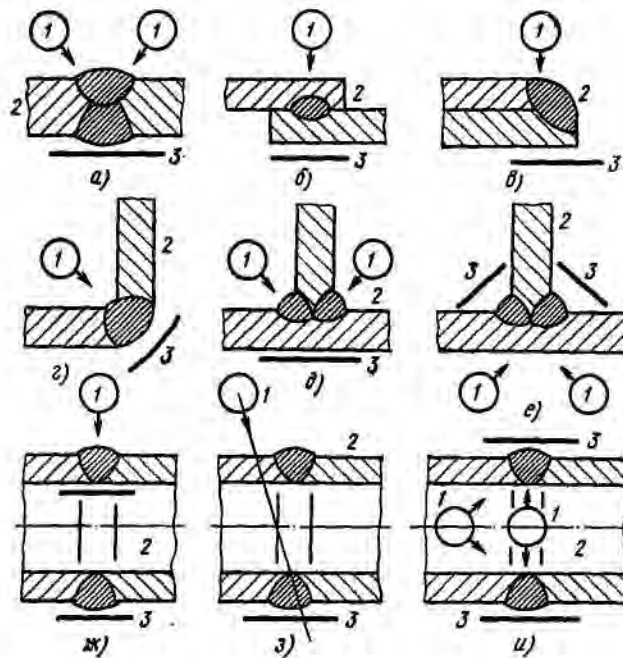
Радиационный контроль качества сварных конструкций: а — встык, б — внахлест; в — е — сварка торцов под разными углами; ж — двух труб встык; з — двух труб при косом расположении источника; и — просвечивание сварных труб изнутри (1 — источник излучения, 2 — сваренные детали, 3 — индикатор)
